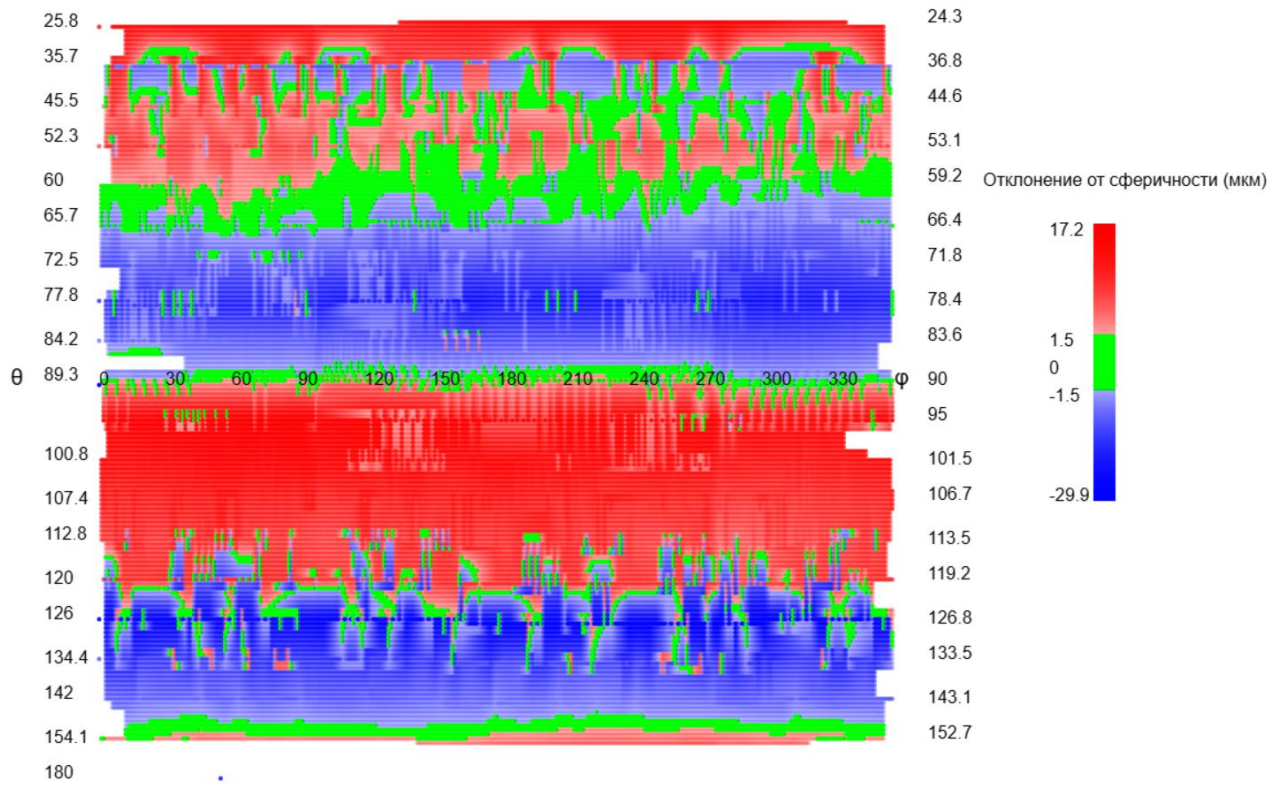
Развертка сферической поверхности шарового пальца №5 до притирки
